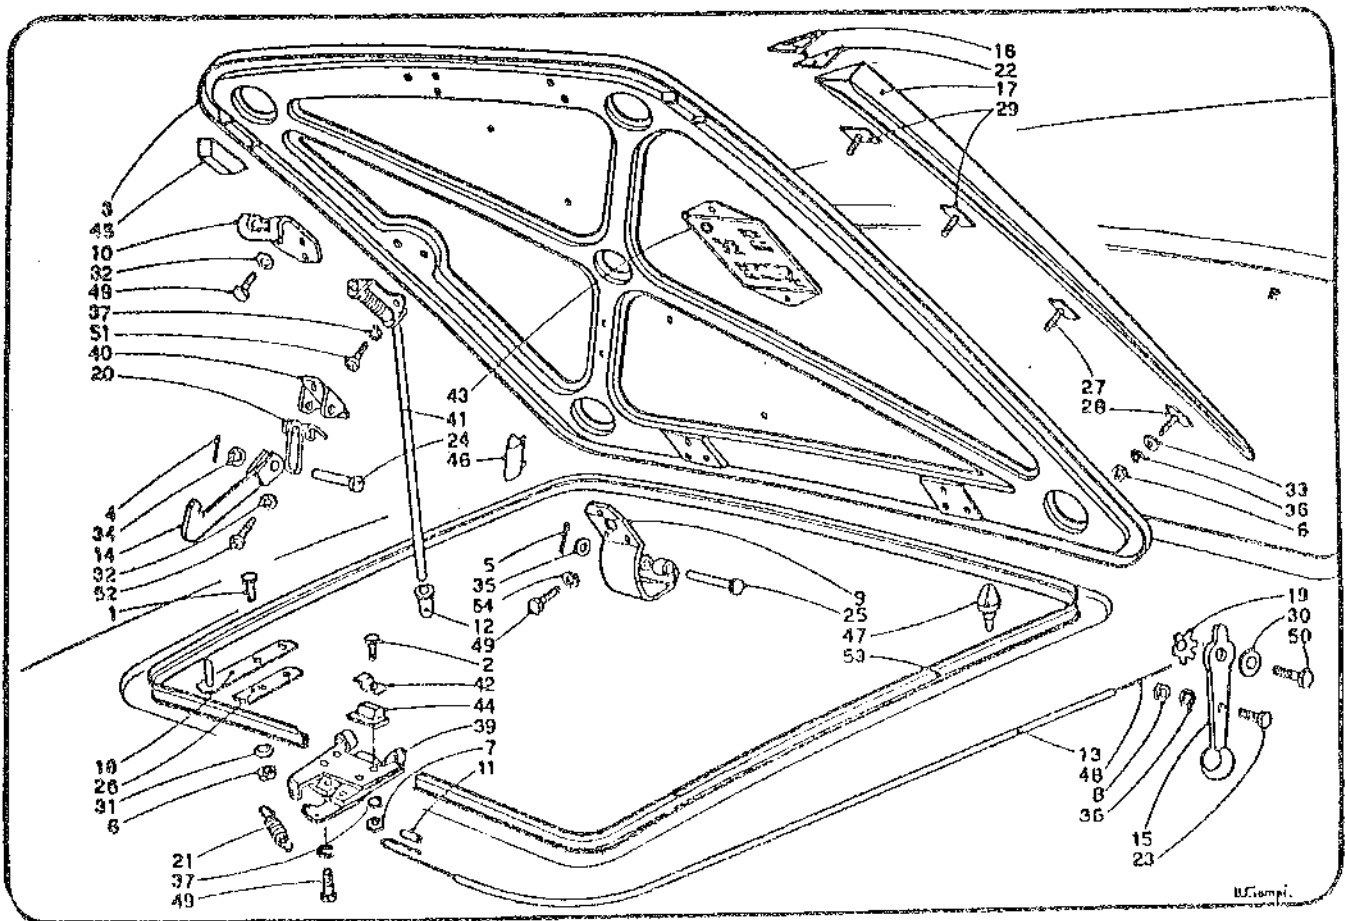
/7 - Capot - Commande ouverture capot - Du Carriage P.D.I.
